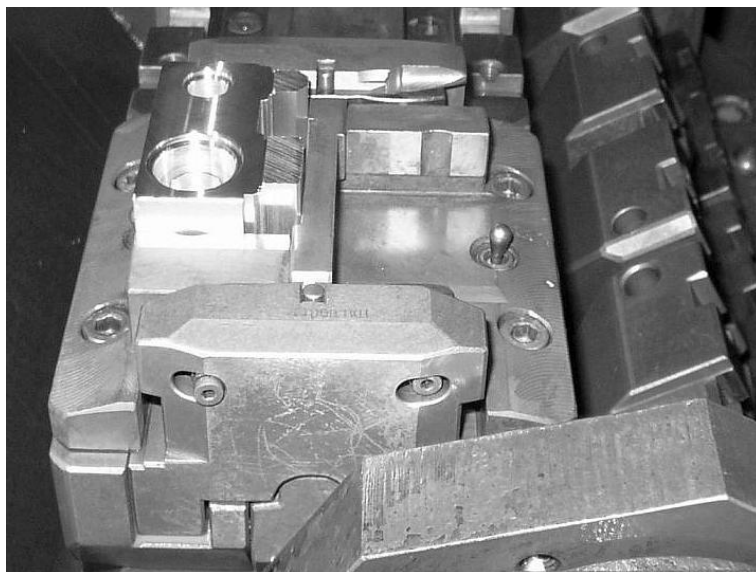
Obráběcí centrum Chiron FZ 12W
